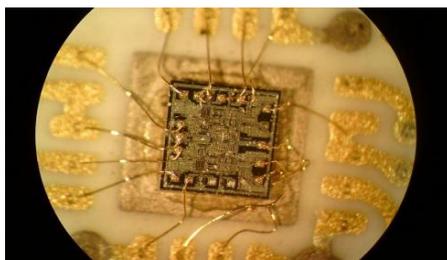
Vznik ohybu, zvlnění mikrodrátku (zdroj: [30])
